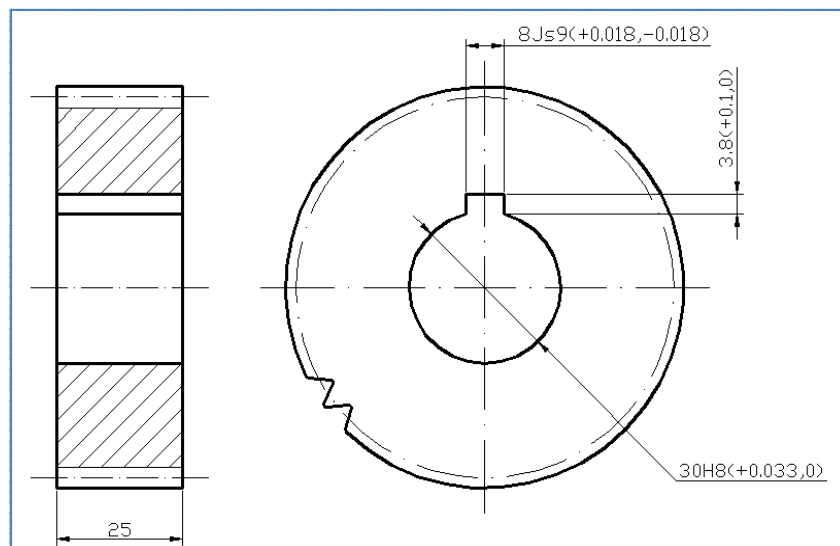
Croquis de las dimensiones iniciales del engranaje
